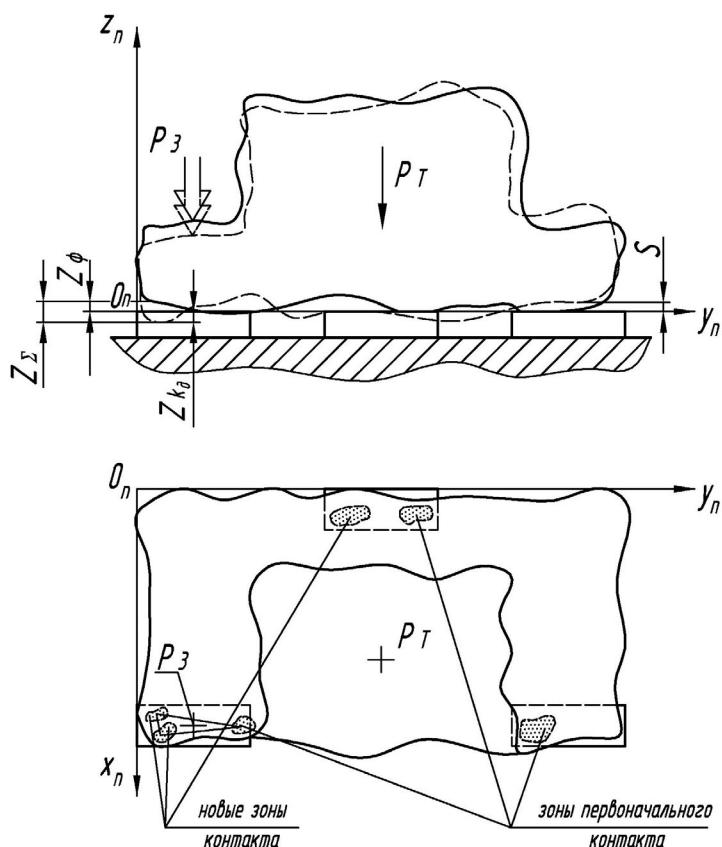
Контактное взаимодействие заготовки с опорами
